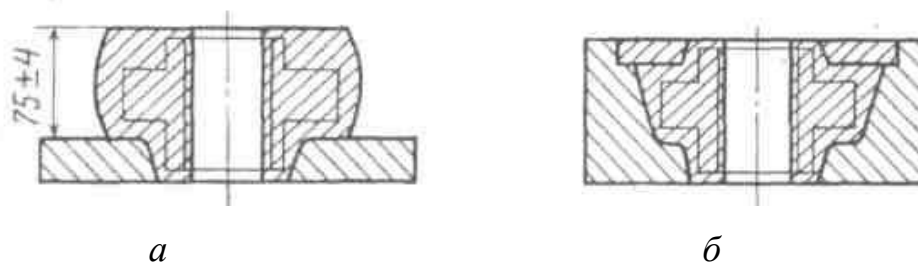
Поковка, полученная: а – ковкой с подкладным кольцом;
